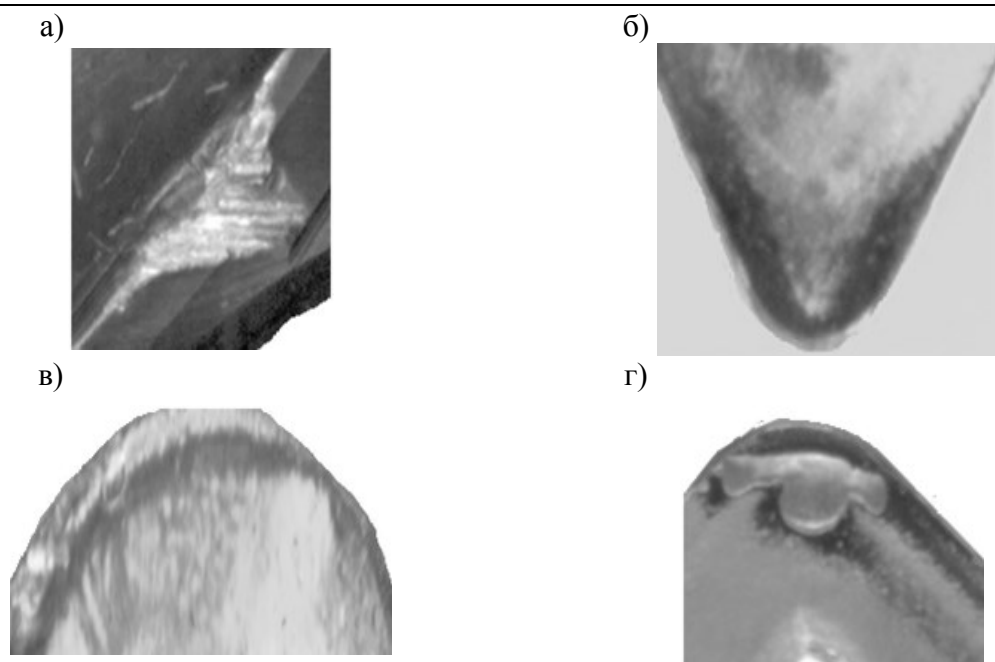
Фотографии изношенных режущих кромок (увеличение $\times 25$): а – концевая фреза (4,22 ч обработки сплава ВТ-23); б – сменная пластина сборной фрезы (3,6 ч обработки стали 12Х18Н10Т); в – сменная пластина сборной фрезы (18,6 ч обработки сплава В-950чТ2); г – сменная пластина сборного резца (3,3 ч обработки стали 30ХГСН2А)
